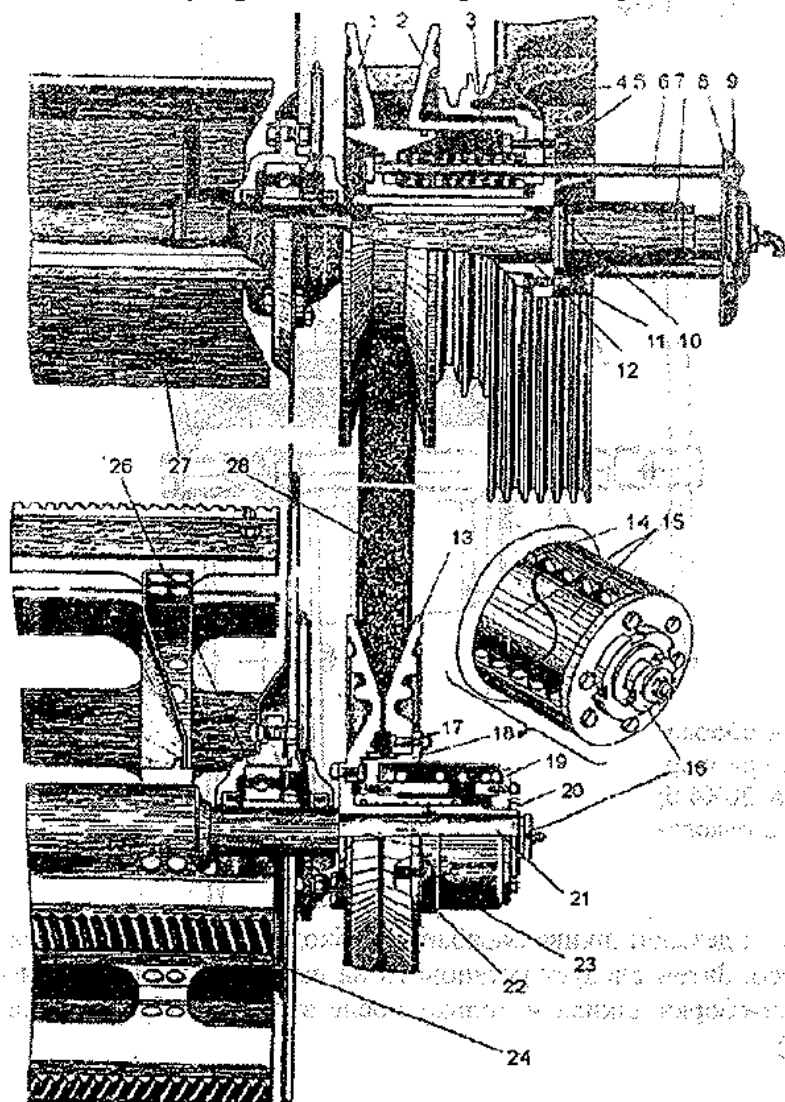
Вариатор барабана: 1 - диск подвижной ведущего шкива; 2 - диск неподвижный; 3, 14 - пружины; 4 - шкив привода молотилки; 5, 17 - ступицы неподвижные; 6 - болт специальный; 7 - гидроцилиндр; 8 - конус; 9, 16, 20 - гайки; 10 - шайба стопорная; 11 - болт регулировочный; 12 - вал бите-ра; 13 - диск ведомого шкива; 15 - муфта; 18 - ступица подвижная; 19 - крышка; 20 - гайка; 21 - вал барабана; 22 - кольцо; 23 - кожух; 24 - барабан молотильный; 26 - одшипник опорный; 27 - бите-р отбойный; 28 - ремень
